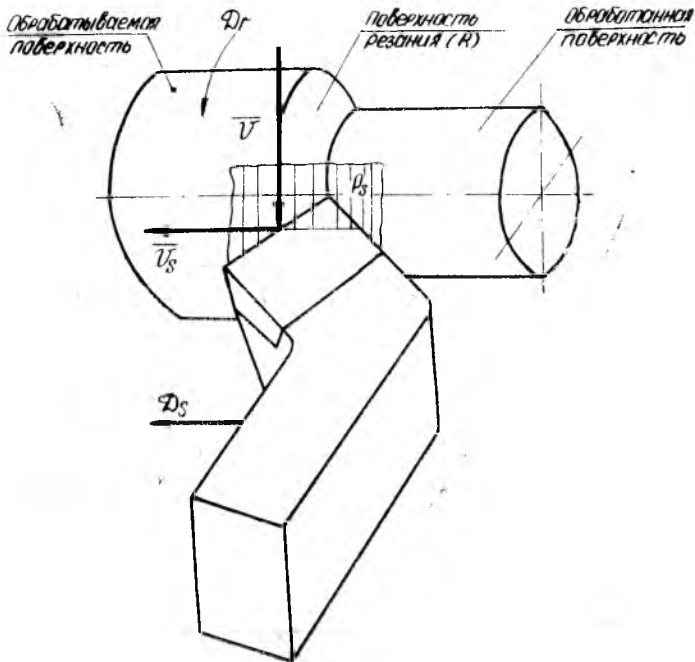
Поверхности заготовки при токарной обработке проходным резцом
